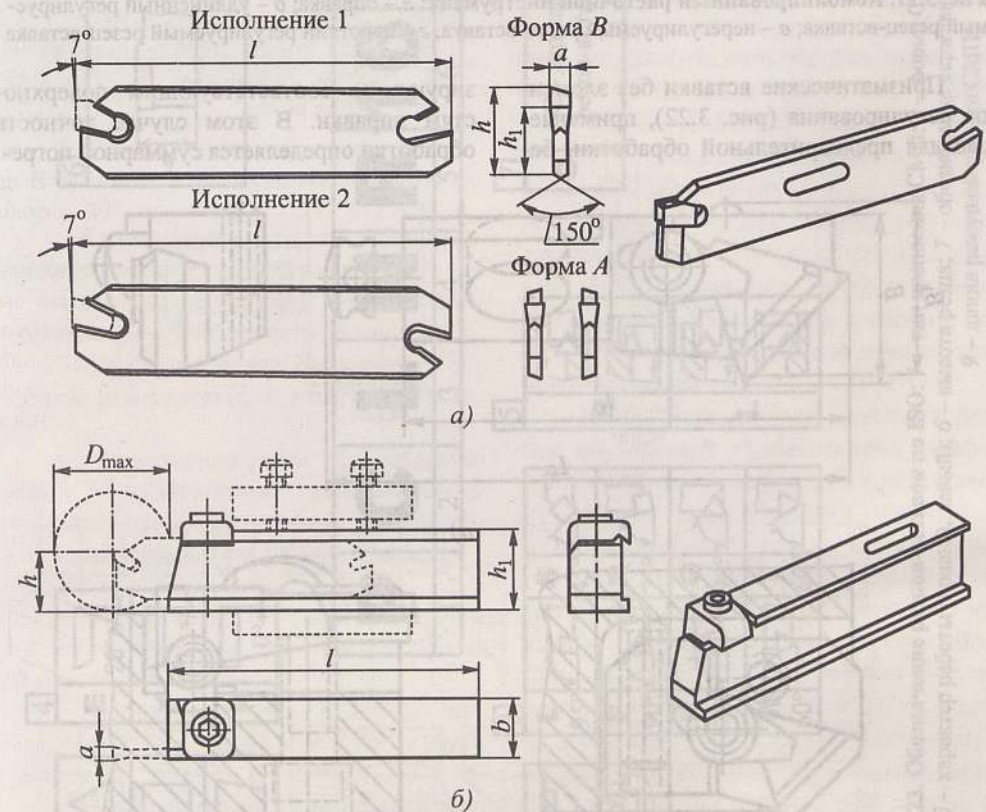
Пластинчатый отрезной резец: а – пластина; б – державка для крепления резца
